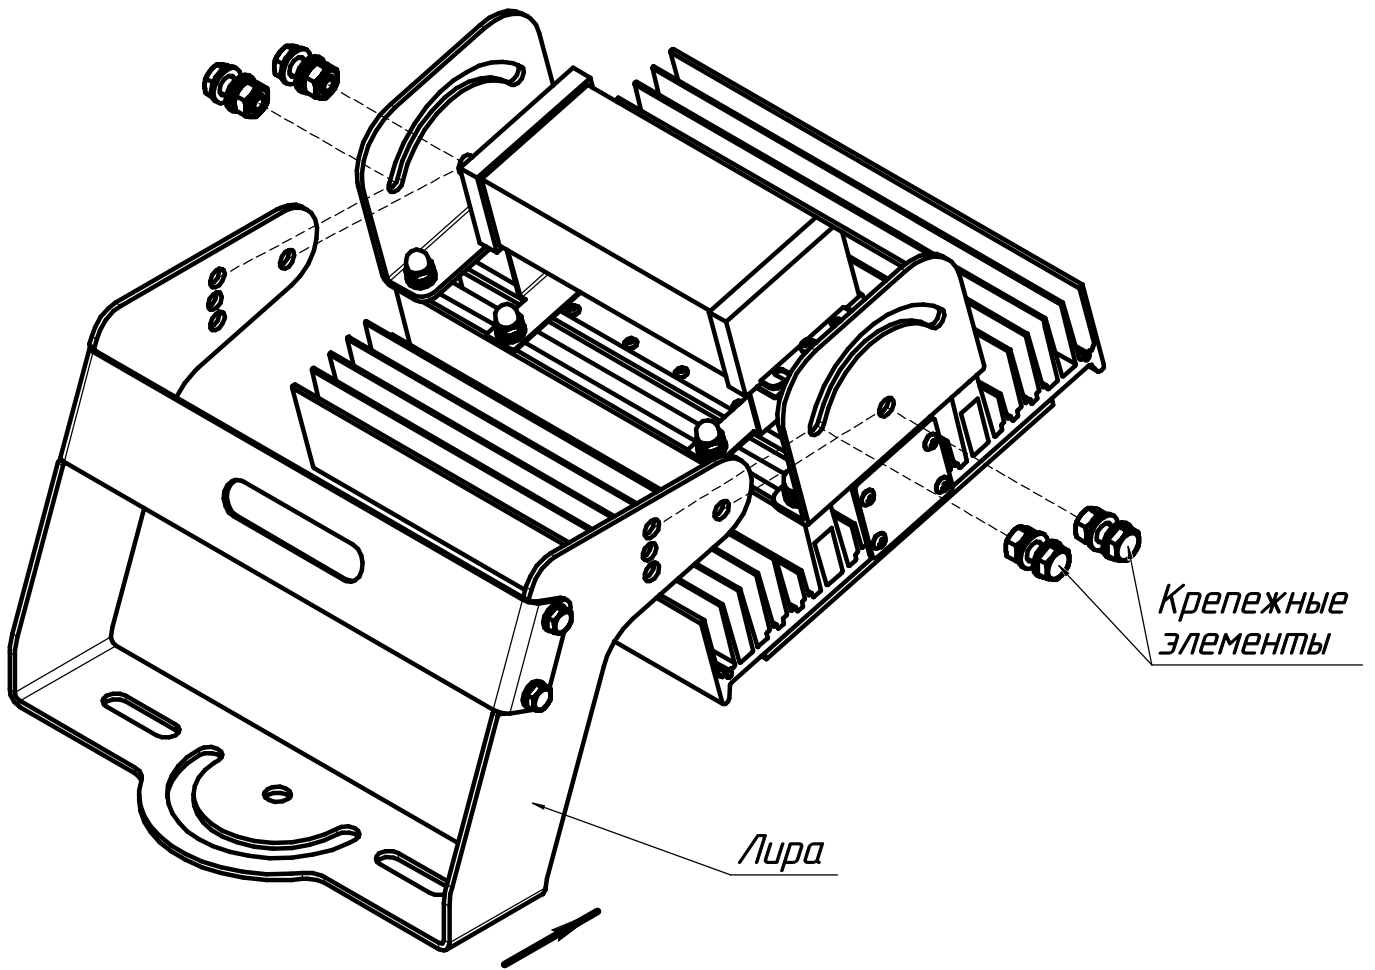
Схема установки узла крепления (лиры) на светильник
